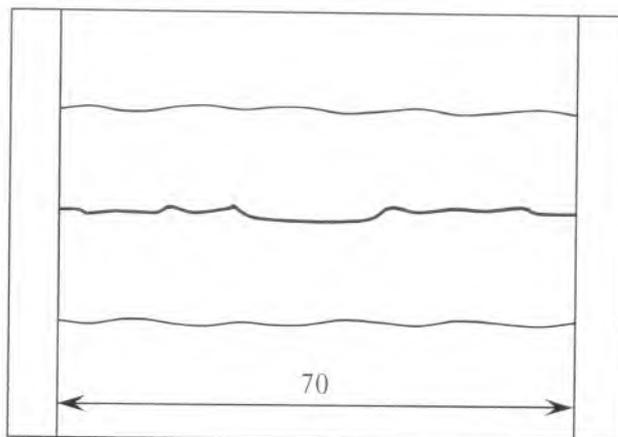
Трещина в стыковом сварном соединении крановых рельсов КР70, эксплуатируемых на открытом воздухе, на поверхности катания, покрытой продуктами коррозии (ржавчиной). Трещина распространяется по всей ширине головки рельса с выходом на боковые поверхности. Ширина поверхности катания 70 мм
